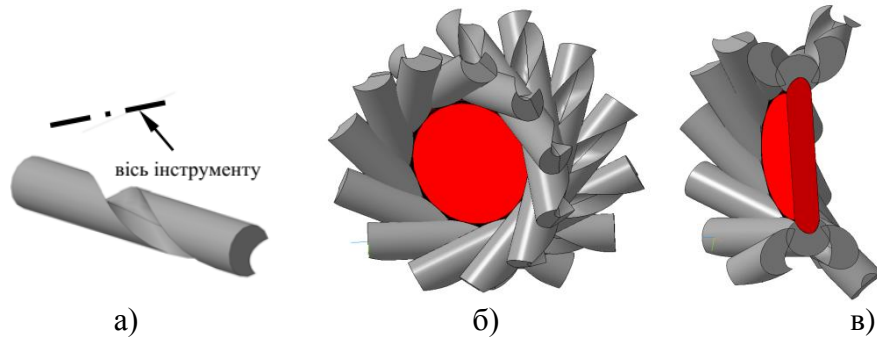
Етапи визначення ВПІ дискового інструменту для обробки гвинтової канавки свердла: а) модель свердла з віссю інструмента, б) побудова послідовних положень деталі – масив по колу, в) визначення осьового перерізу ВПІ дискового інструменту.
